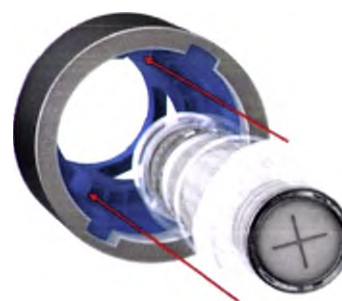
Стыковка держателя картриджа и фиксирующего кольца
